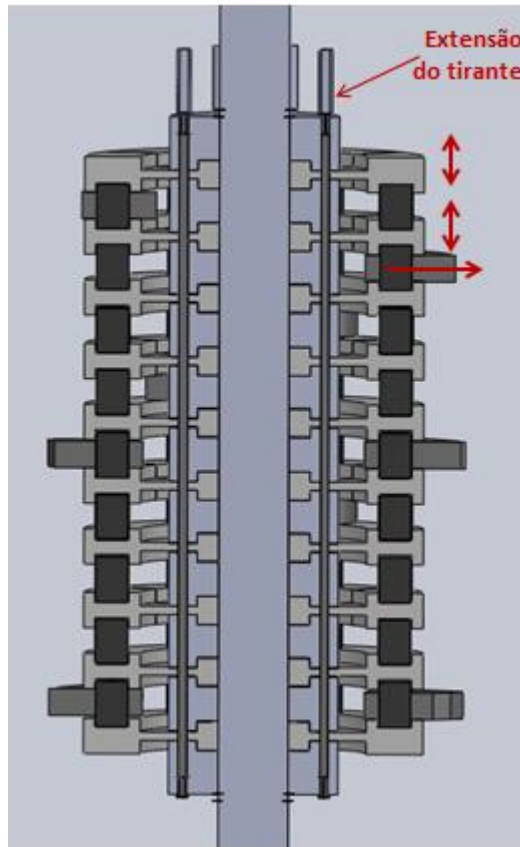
Vista em corte do rotor na sua posição de manutenção.
